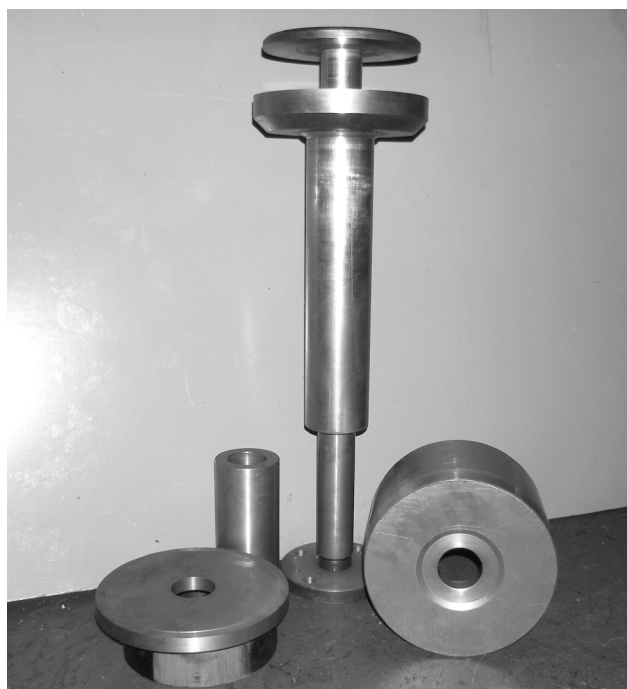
Общий вид элементов режущей-деформирующей прошивки
